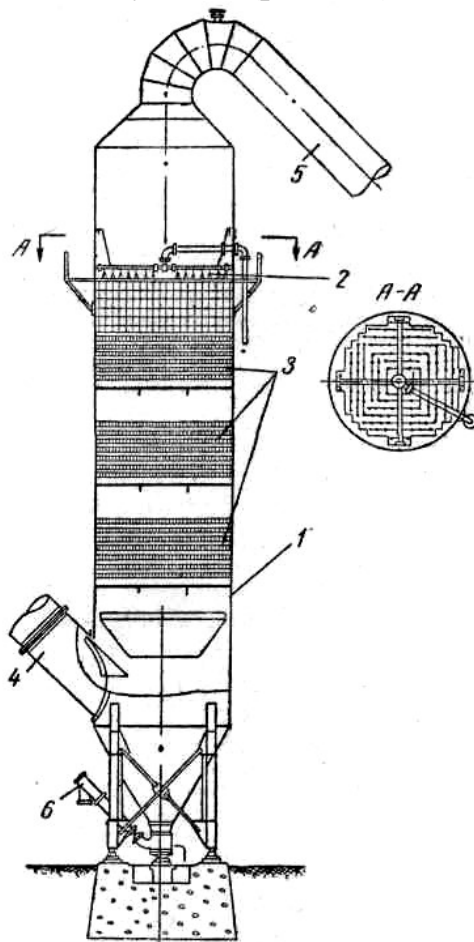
Схема скруббера: 1 – корпус; 2 – брызгало; 3 – насадки; 4 – труба для входа газов; 5 – труба для выхода газов; 6 – устройство для выгрузки пыли
